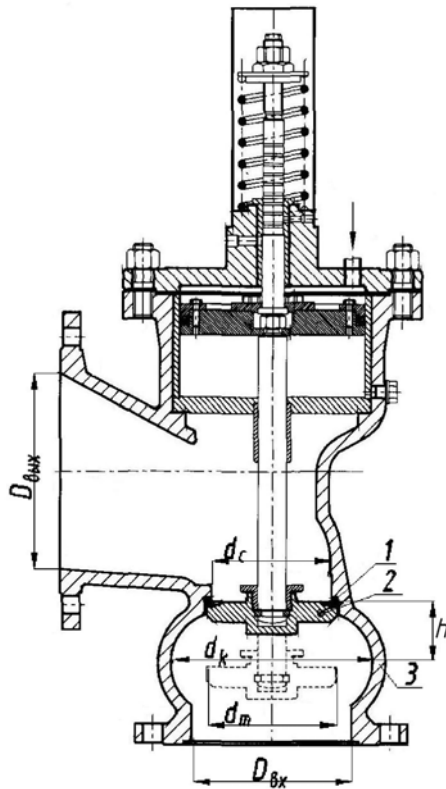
Предохранительный клапан: 1 – седло; 2 – тарелка; 3 – корпус
